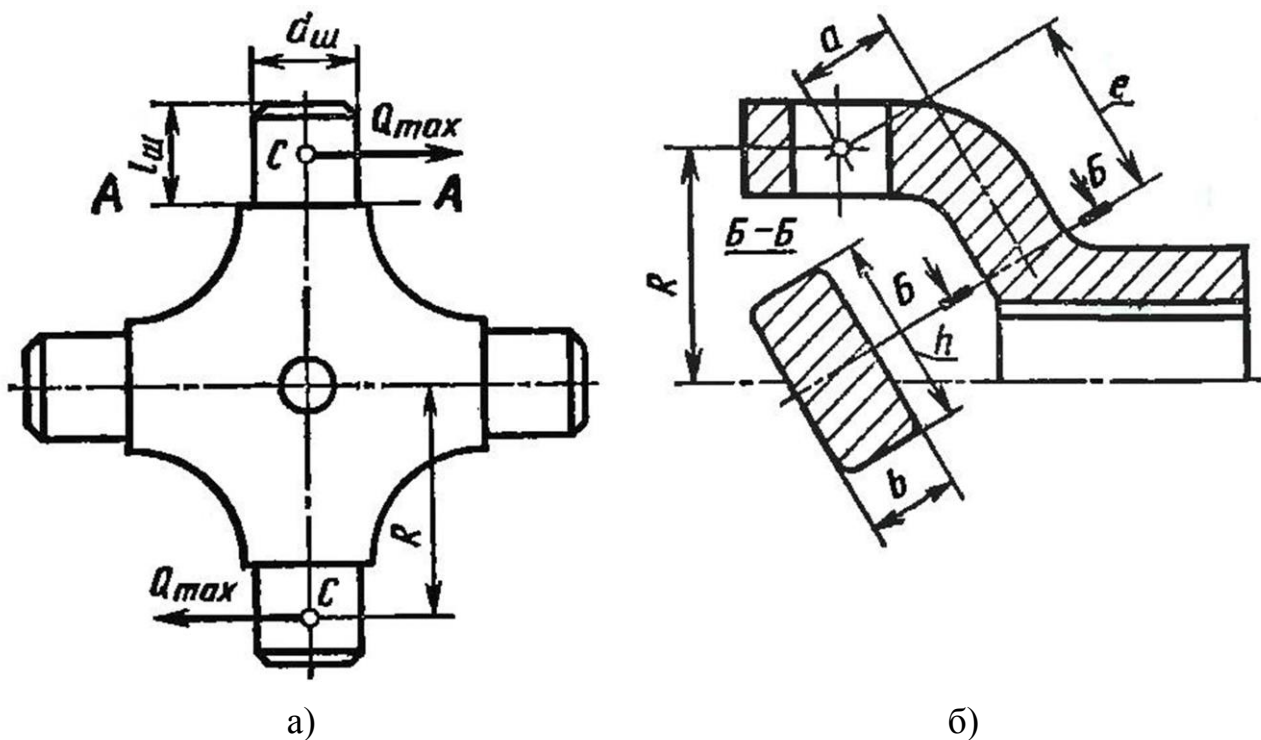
Розрахункова схема вилки і хрестовини
